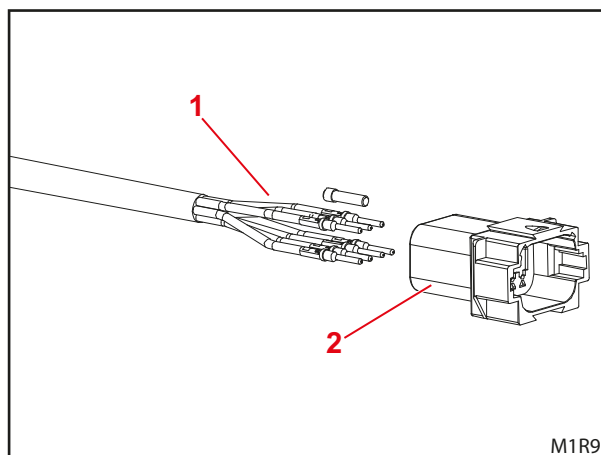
Conector enchufable de 8 polos sin "salientes" para el montaje en la parte inferior de Hydro-Fix
